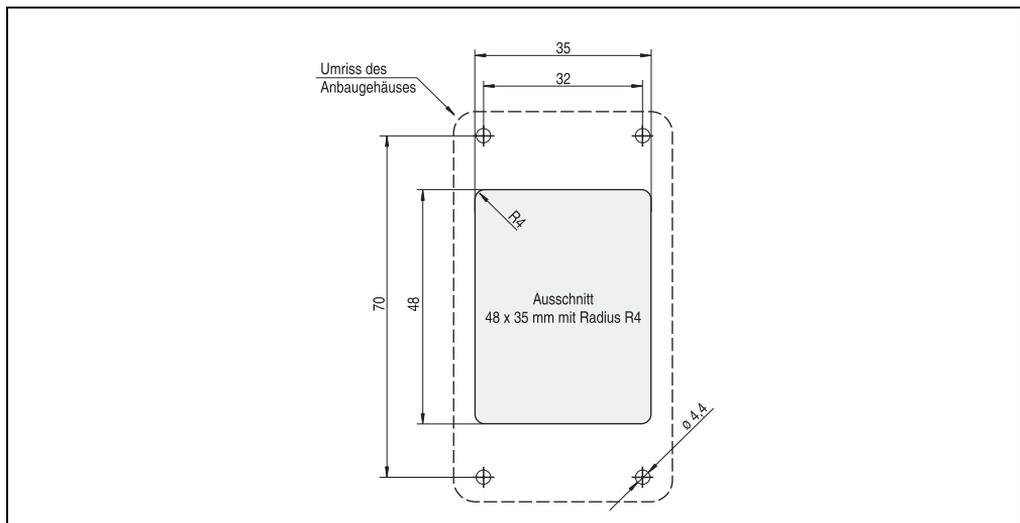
Bohrschablone für die Schaltschrankbuchse
